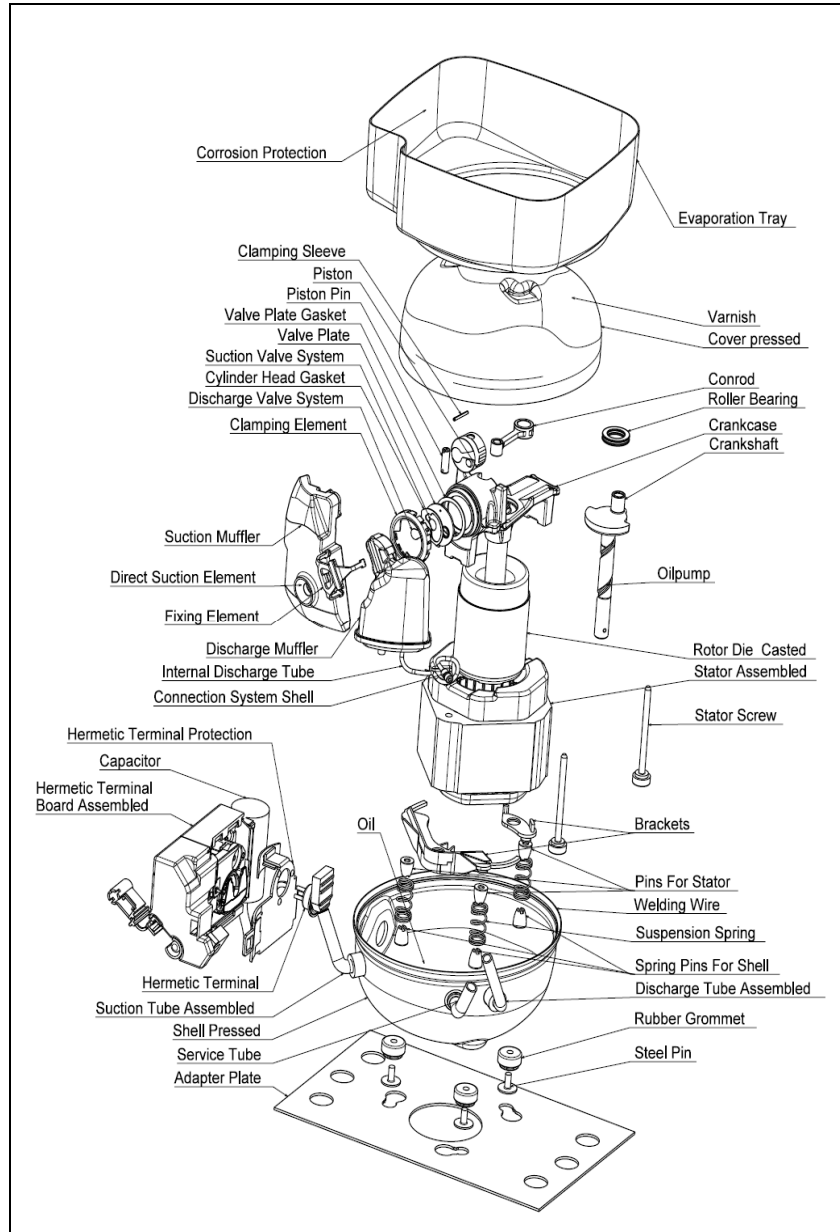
Explosionszeichnung des Delta Kompressors [Kerschbaumer K. 2011, S.4]
